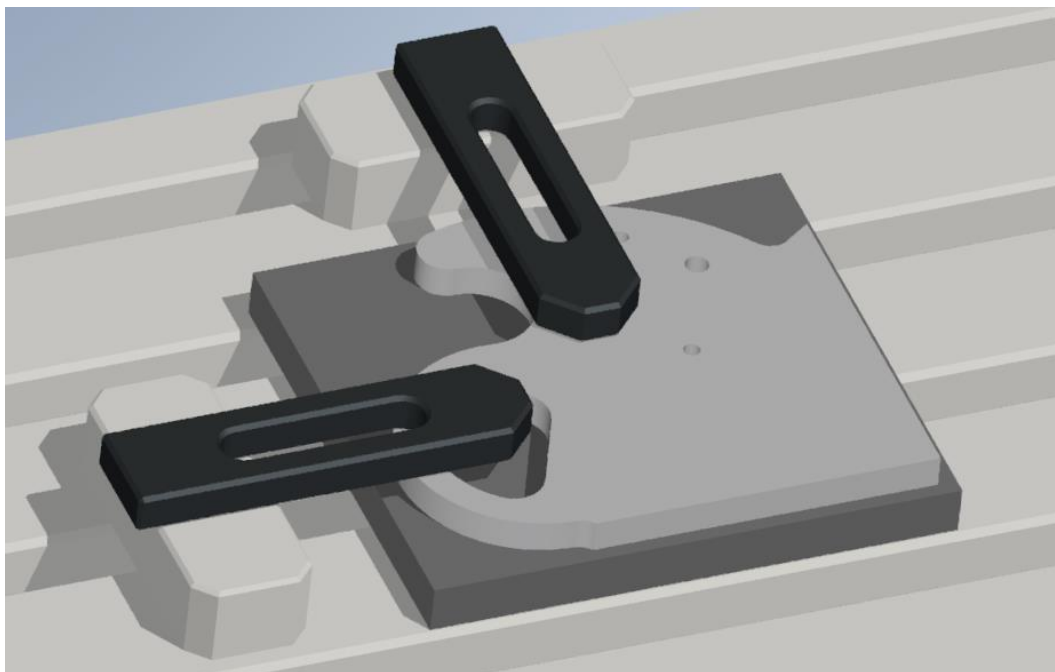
3D model upnutí polotovaru velké kladky.
